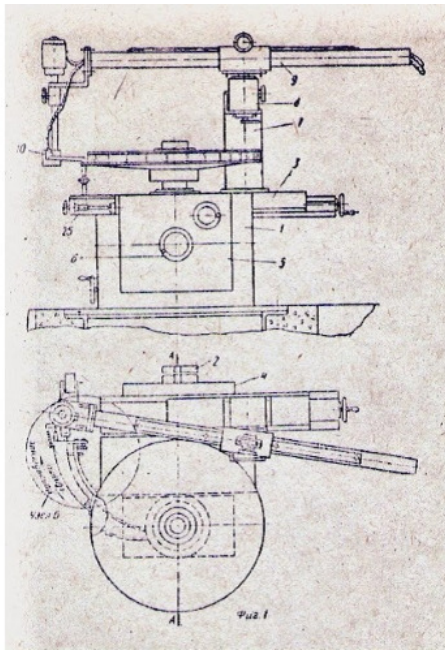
Устройство для автоматической приварки лопастей к ведущему и покрывному дискам рабочего колеса центробежной воздуходувной машины
